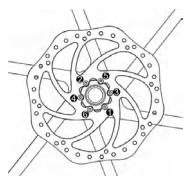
Séquence de serrage du disque et des vis de fixation du disque
